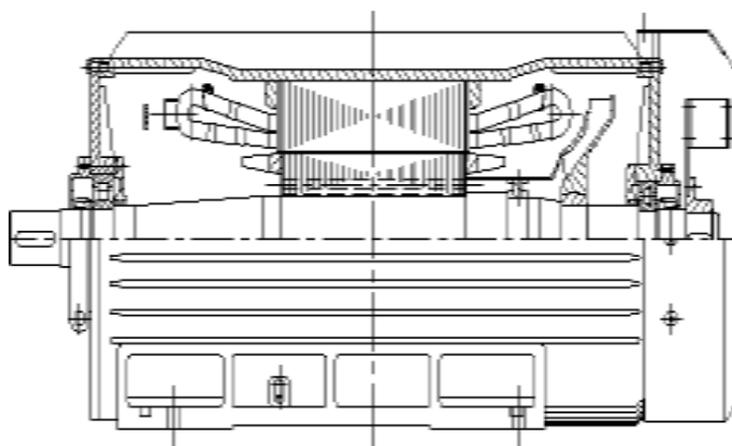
Сборочный чертеж двигателя с методом охлаждения IC411
